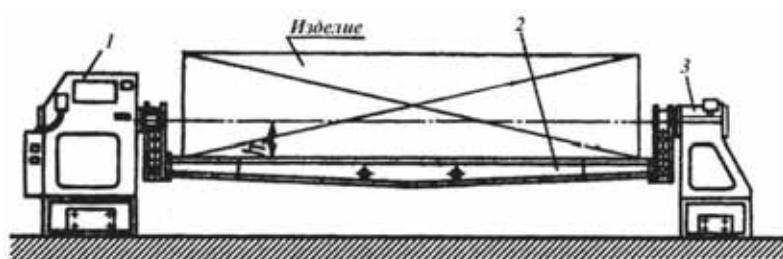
Сварочный кантователь: 1 – приводная стойка; 2 – силовая балка; 3 – стойка
